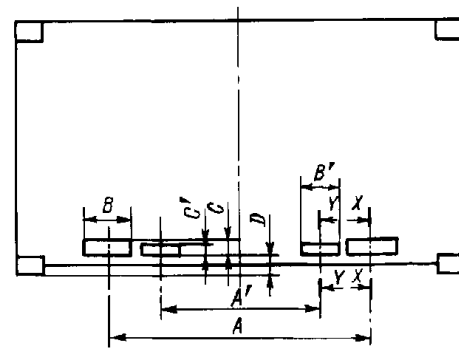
Расположение и размеры карманов для вилочных захватов
